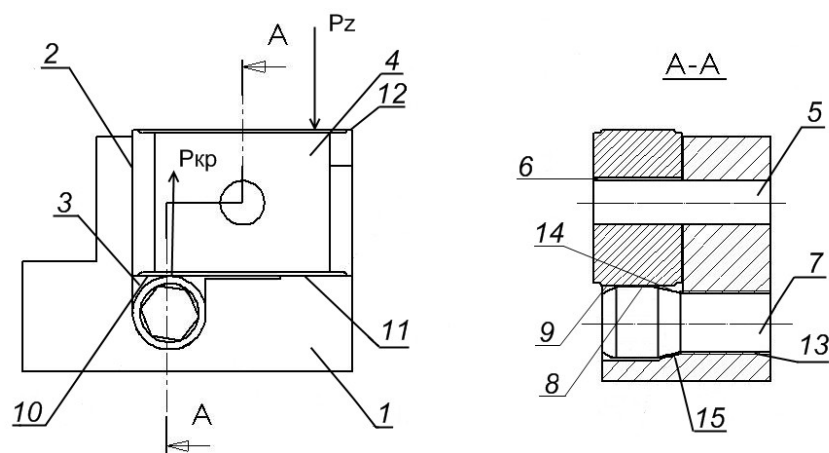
Усовершенствованная конструкция сборного резца с тангенциальным расположением пластины
